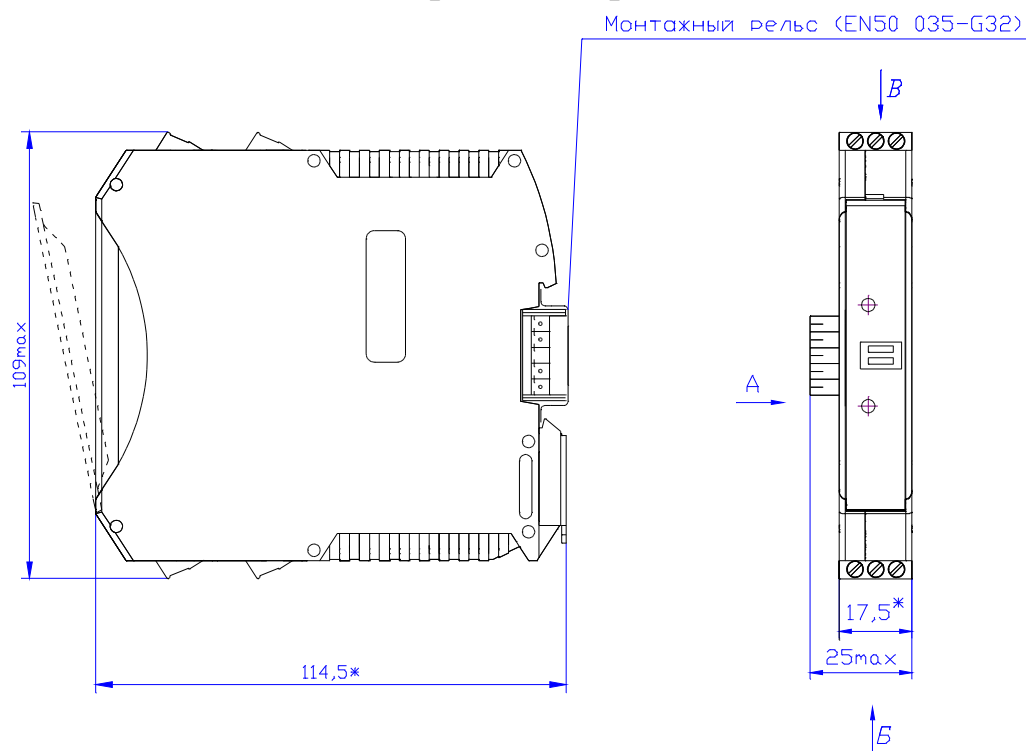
Габаритный чертеж модуля EF 24DC/24DC-0,05 2
